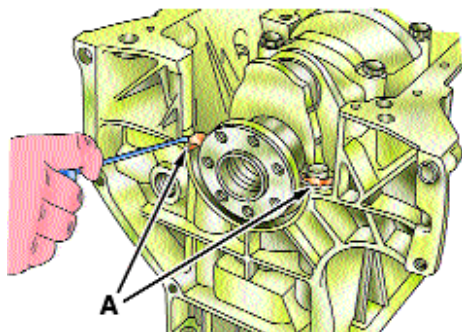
Нанесение герметика на посадочные места крышки 1-го коренного подшипника коленчатого вала двигателя F3R 272
